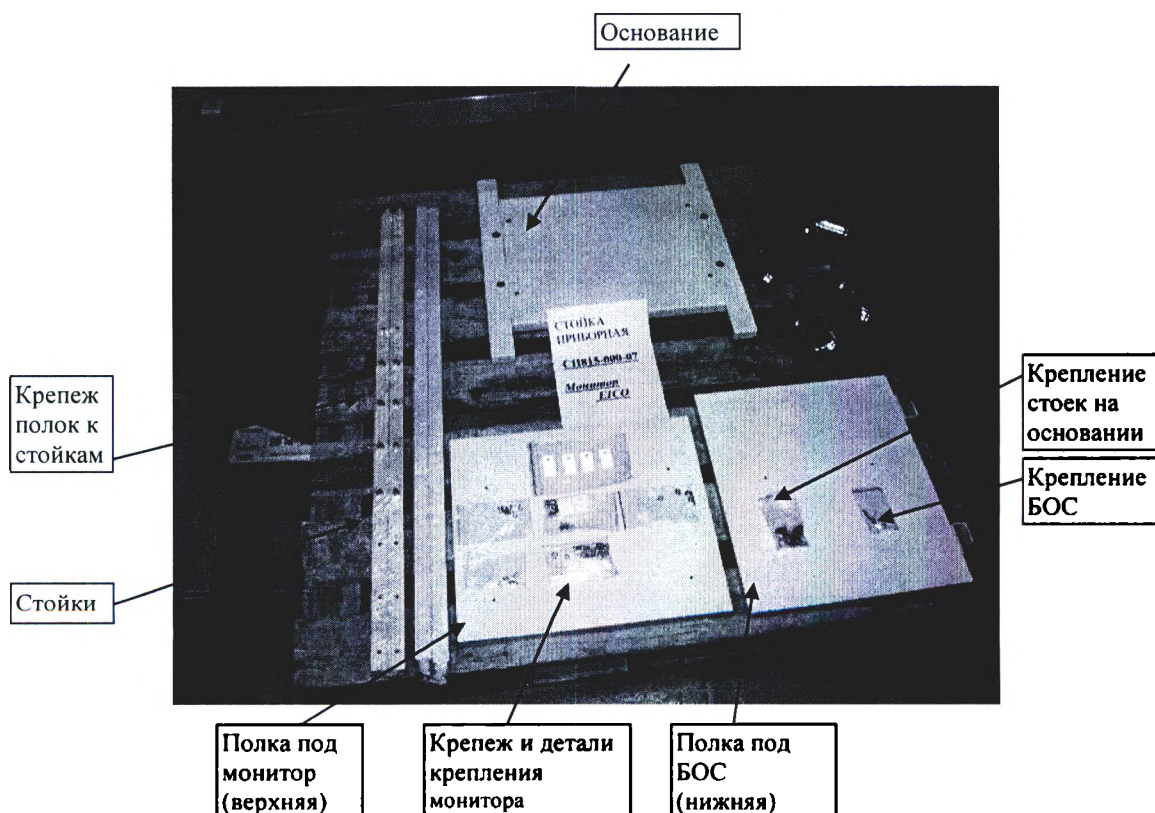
Сборка стойки СП815- 000 под монитор
